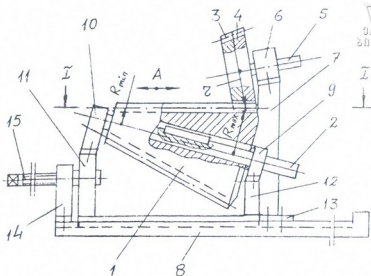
Одноступенчатый вариатор с коническими зубчатыми колесами
